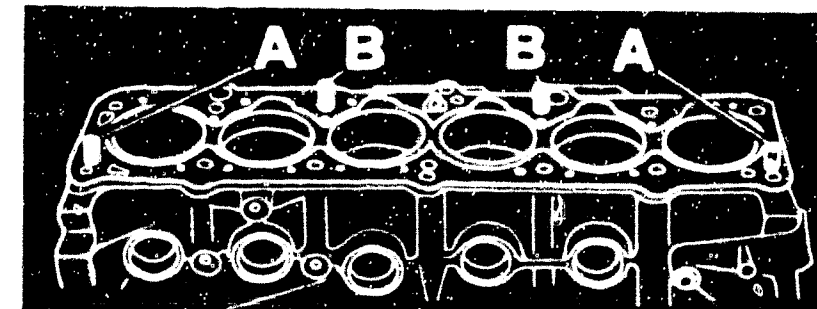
Motoren D 24, D 24 T: Beim Auflegen des Zylinderkopfs sind immer 4 Passtifte (Werkzeugnummer 5234) zu verwenden. Die Stifte A führen die Dichtung und die Stifte B den Zylinderkopf.
